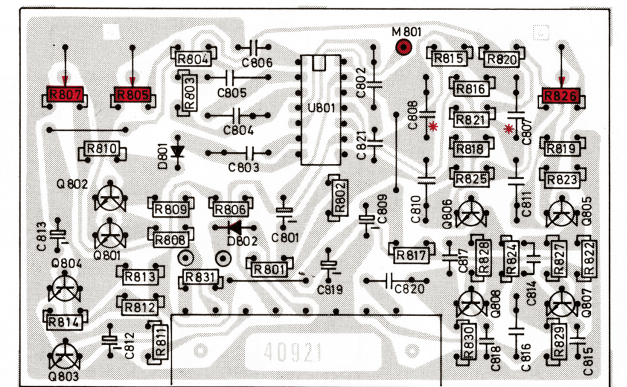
Plate (1. utgave) for stereodekoder 5-3 (sett fra loddessiden), brukt på en del Huldra 10 mottakere
